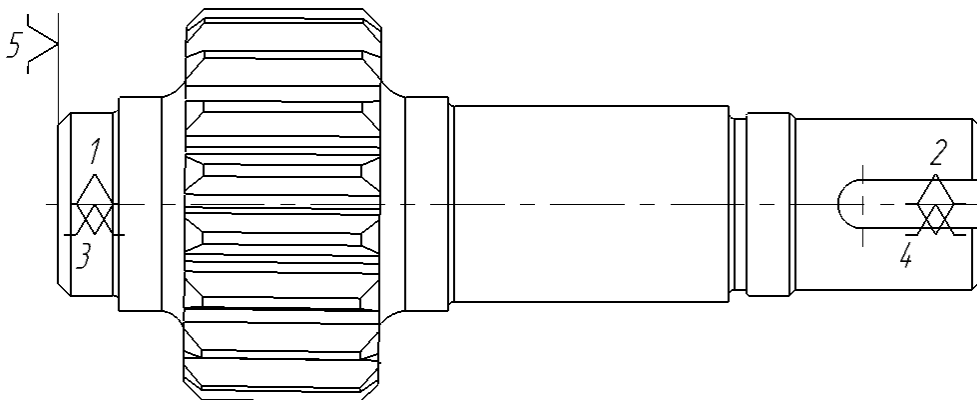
Теоретична схема базування деталі «Вал-шестерня» по загальній технологічній базі (ЗТБ)
